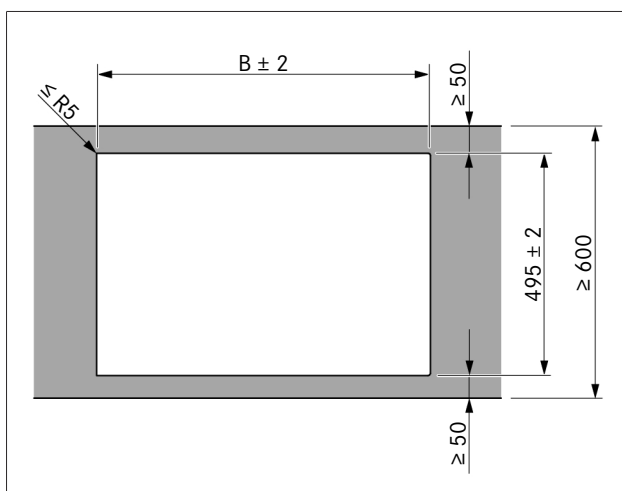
Rozmery drážky pre zapustenú montáž
